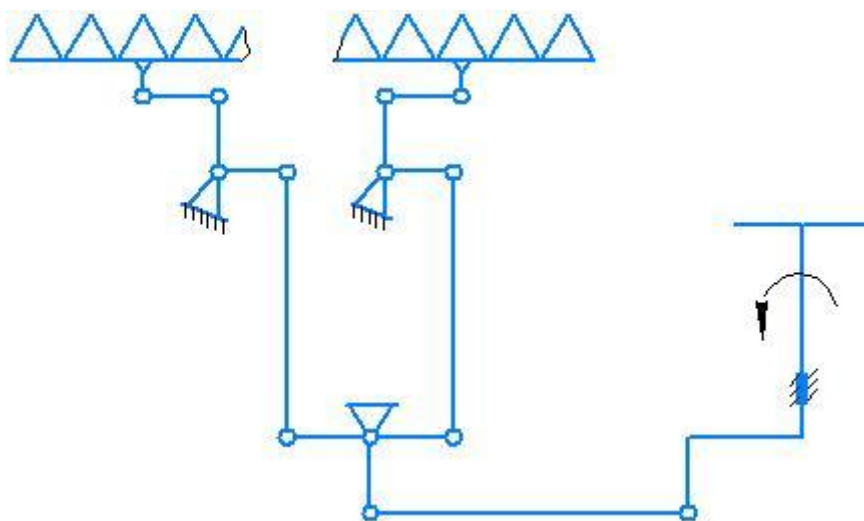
Беспальцевый режущий аппаратов с двумя подвижными ножами
